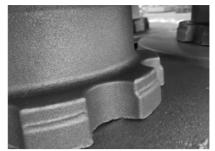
改善后的铸件表面情况 Fig.7 Surface condition of the improved casting
